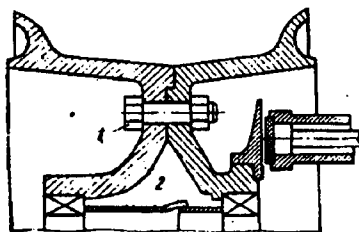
Корпус колеса передней опоры (разъемный): 1 – болты соединения частей колеса; 2 – распорная втулка
